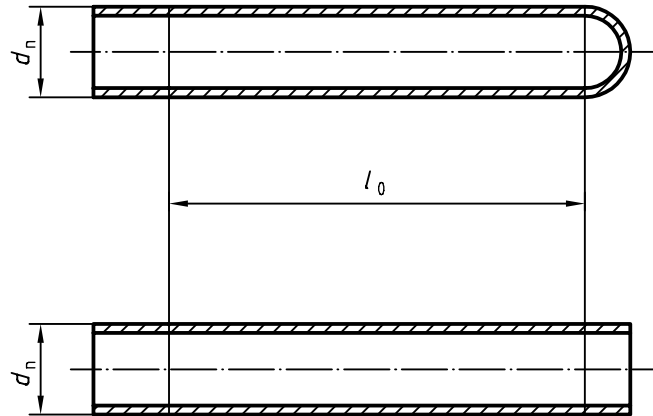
Éprouvettes obtenues par moulage par injection (épreuve supérieure) et par extrusion (épreuve inférieure)
